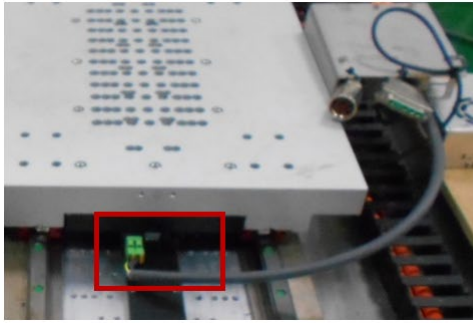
Bevestig de verlengkabel met een kabelbinder en steek hem in de kabelketting
